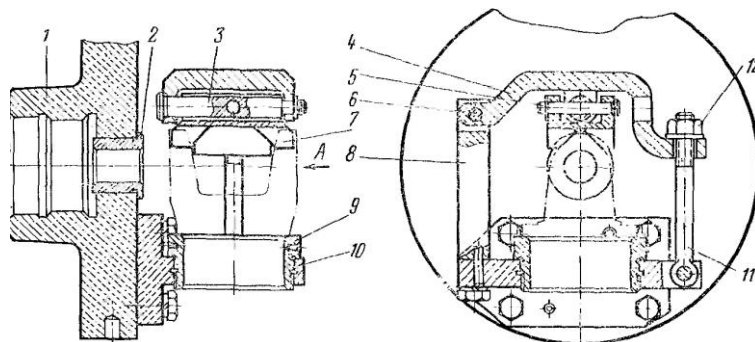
Пристосування для розточування отворів у вилках під підшипники хрестовини карданного валу:
